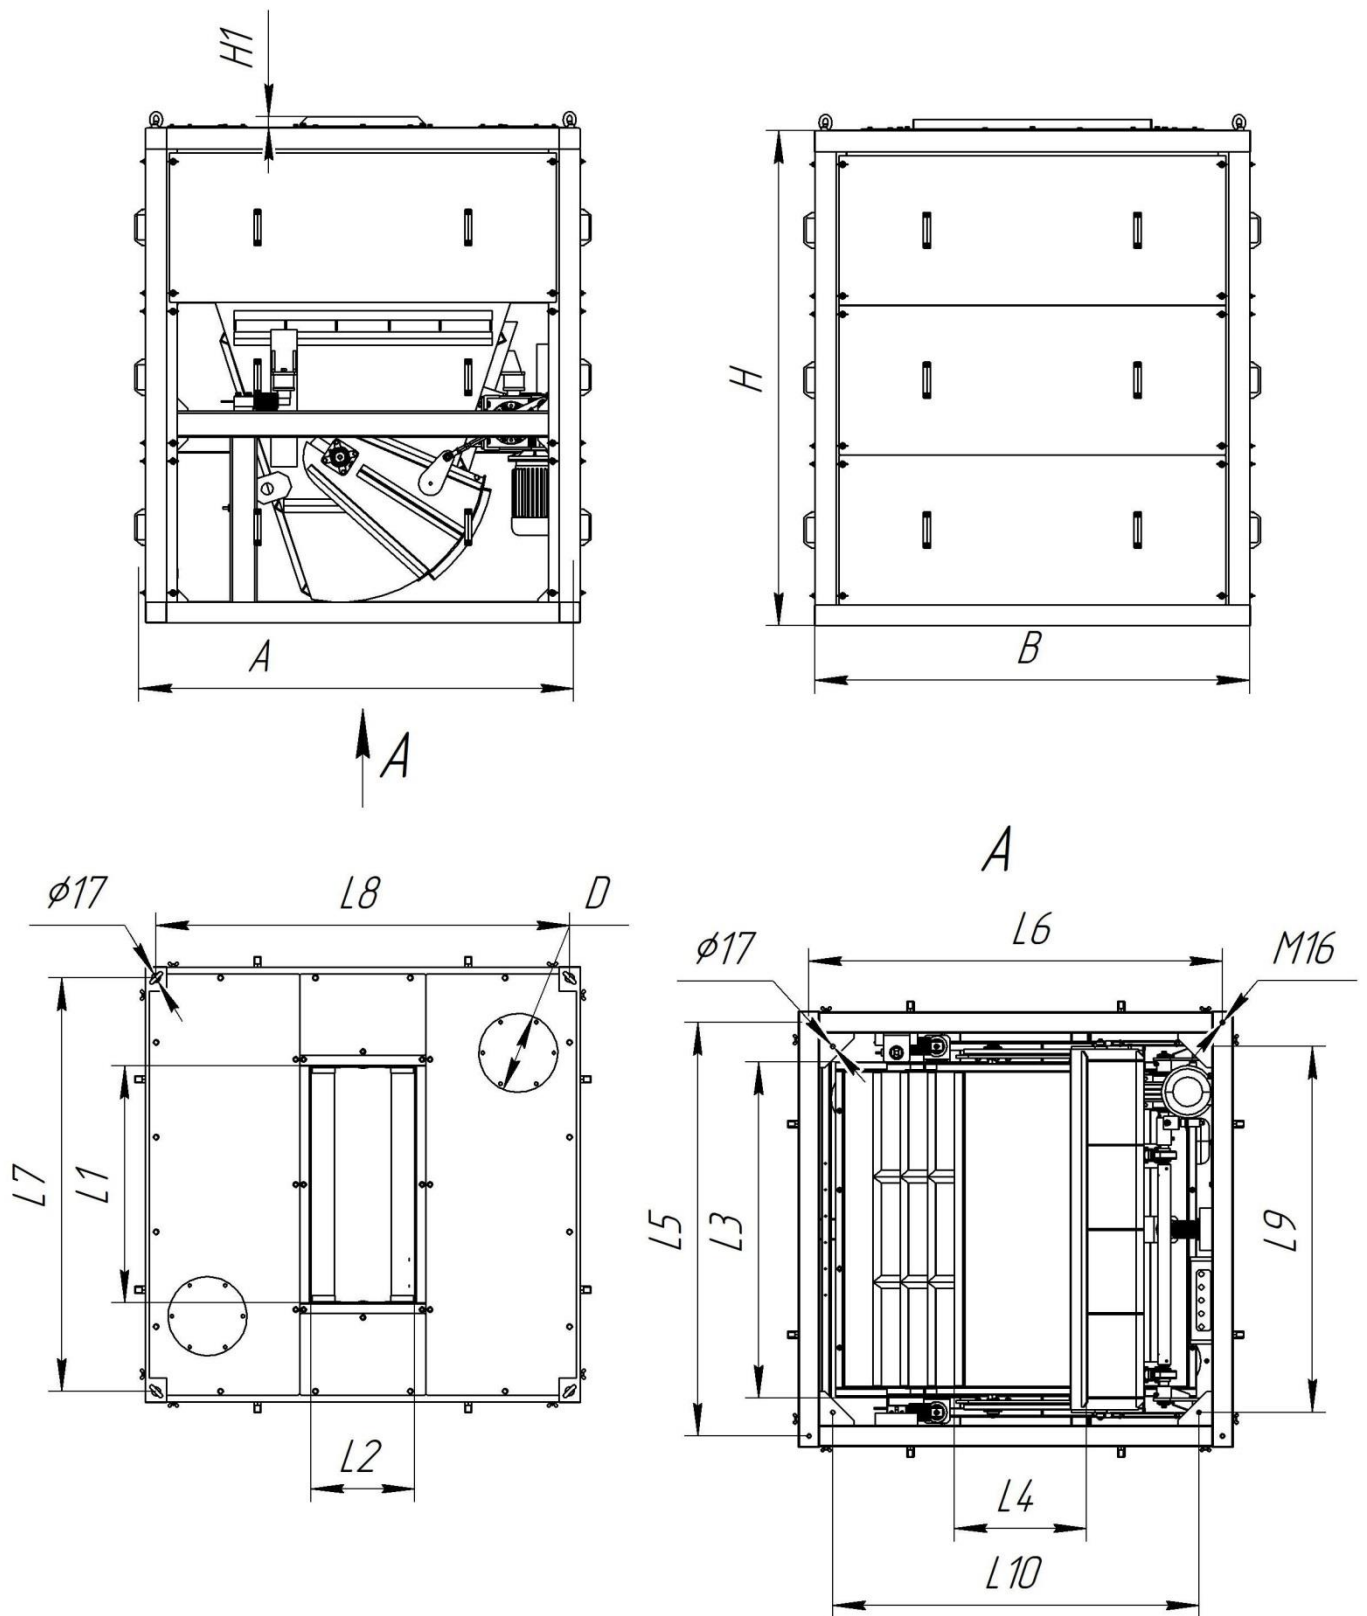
Габаритные и присоединительные размеры весов типа MB5
